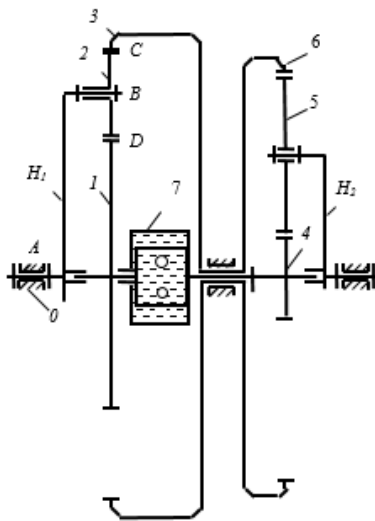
Уравновешенный двух подвижных зубчатый адаптивный вариатор
